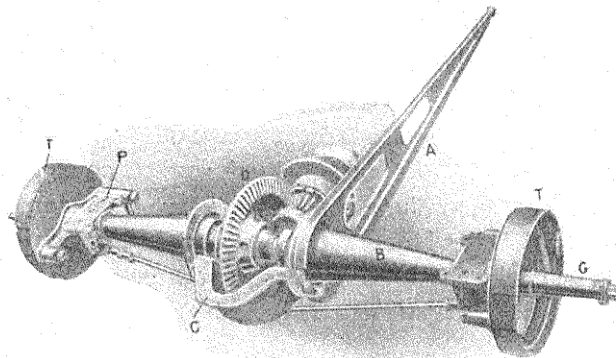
Ensemble d'un pont arrière F. N. (transmission par cardan).
